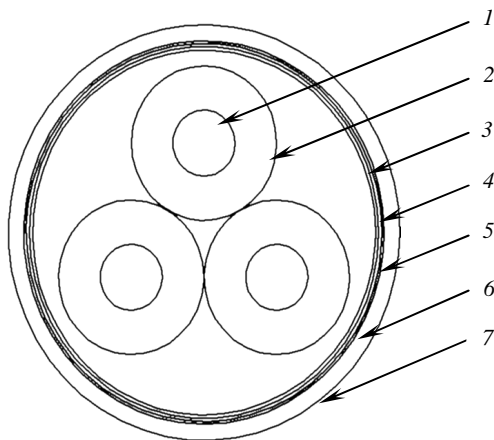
Кабель марки ВВГ на напряжение 6 кВ: 1 – медная токопроводящая жила; 2 – изоляция из поливинилхлоридного пластика (ПВХ); 3 – поясная изоляция из ПВХ-пластиката; 4 – электропроводящий экран из электропроводящего материала; 5 – металлический экран из двух медных лент; 6 – разделительный слой: две ленты из ПВХ-пластиката; 7 – оболочка из ПВХ-пластиката
